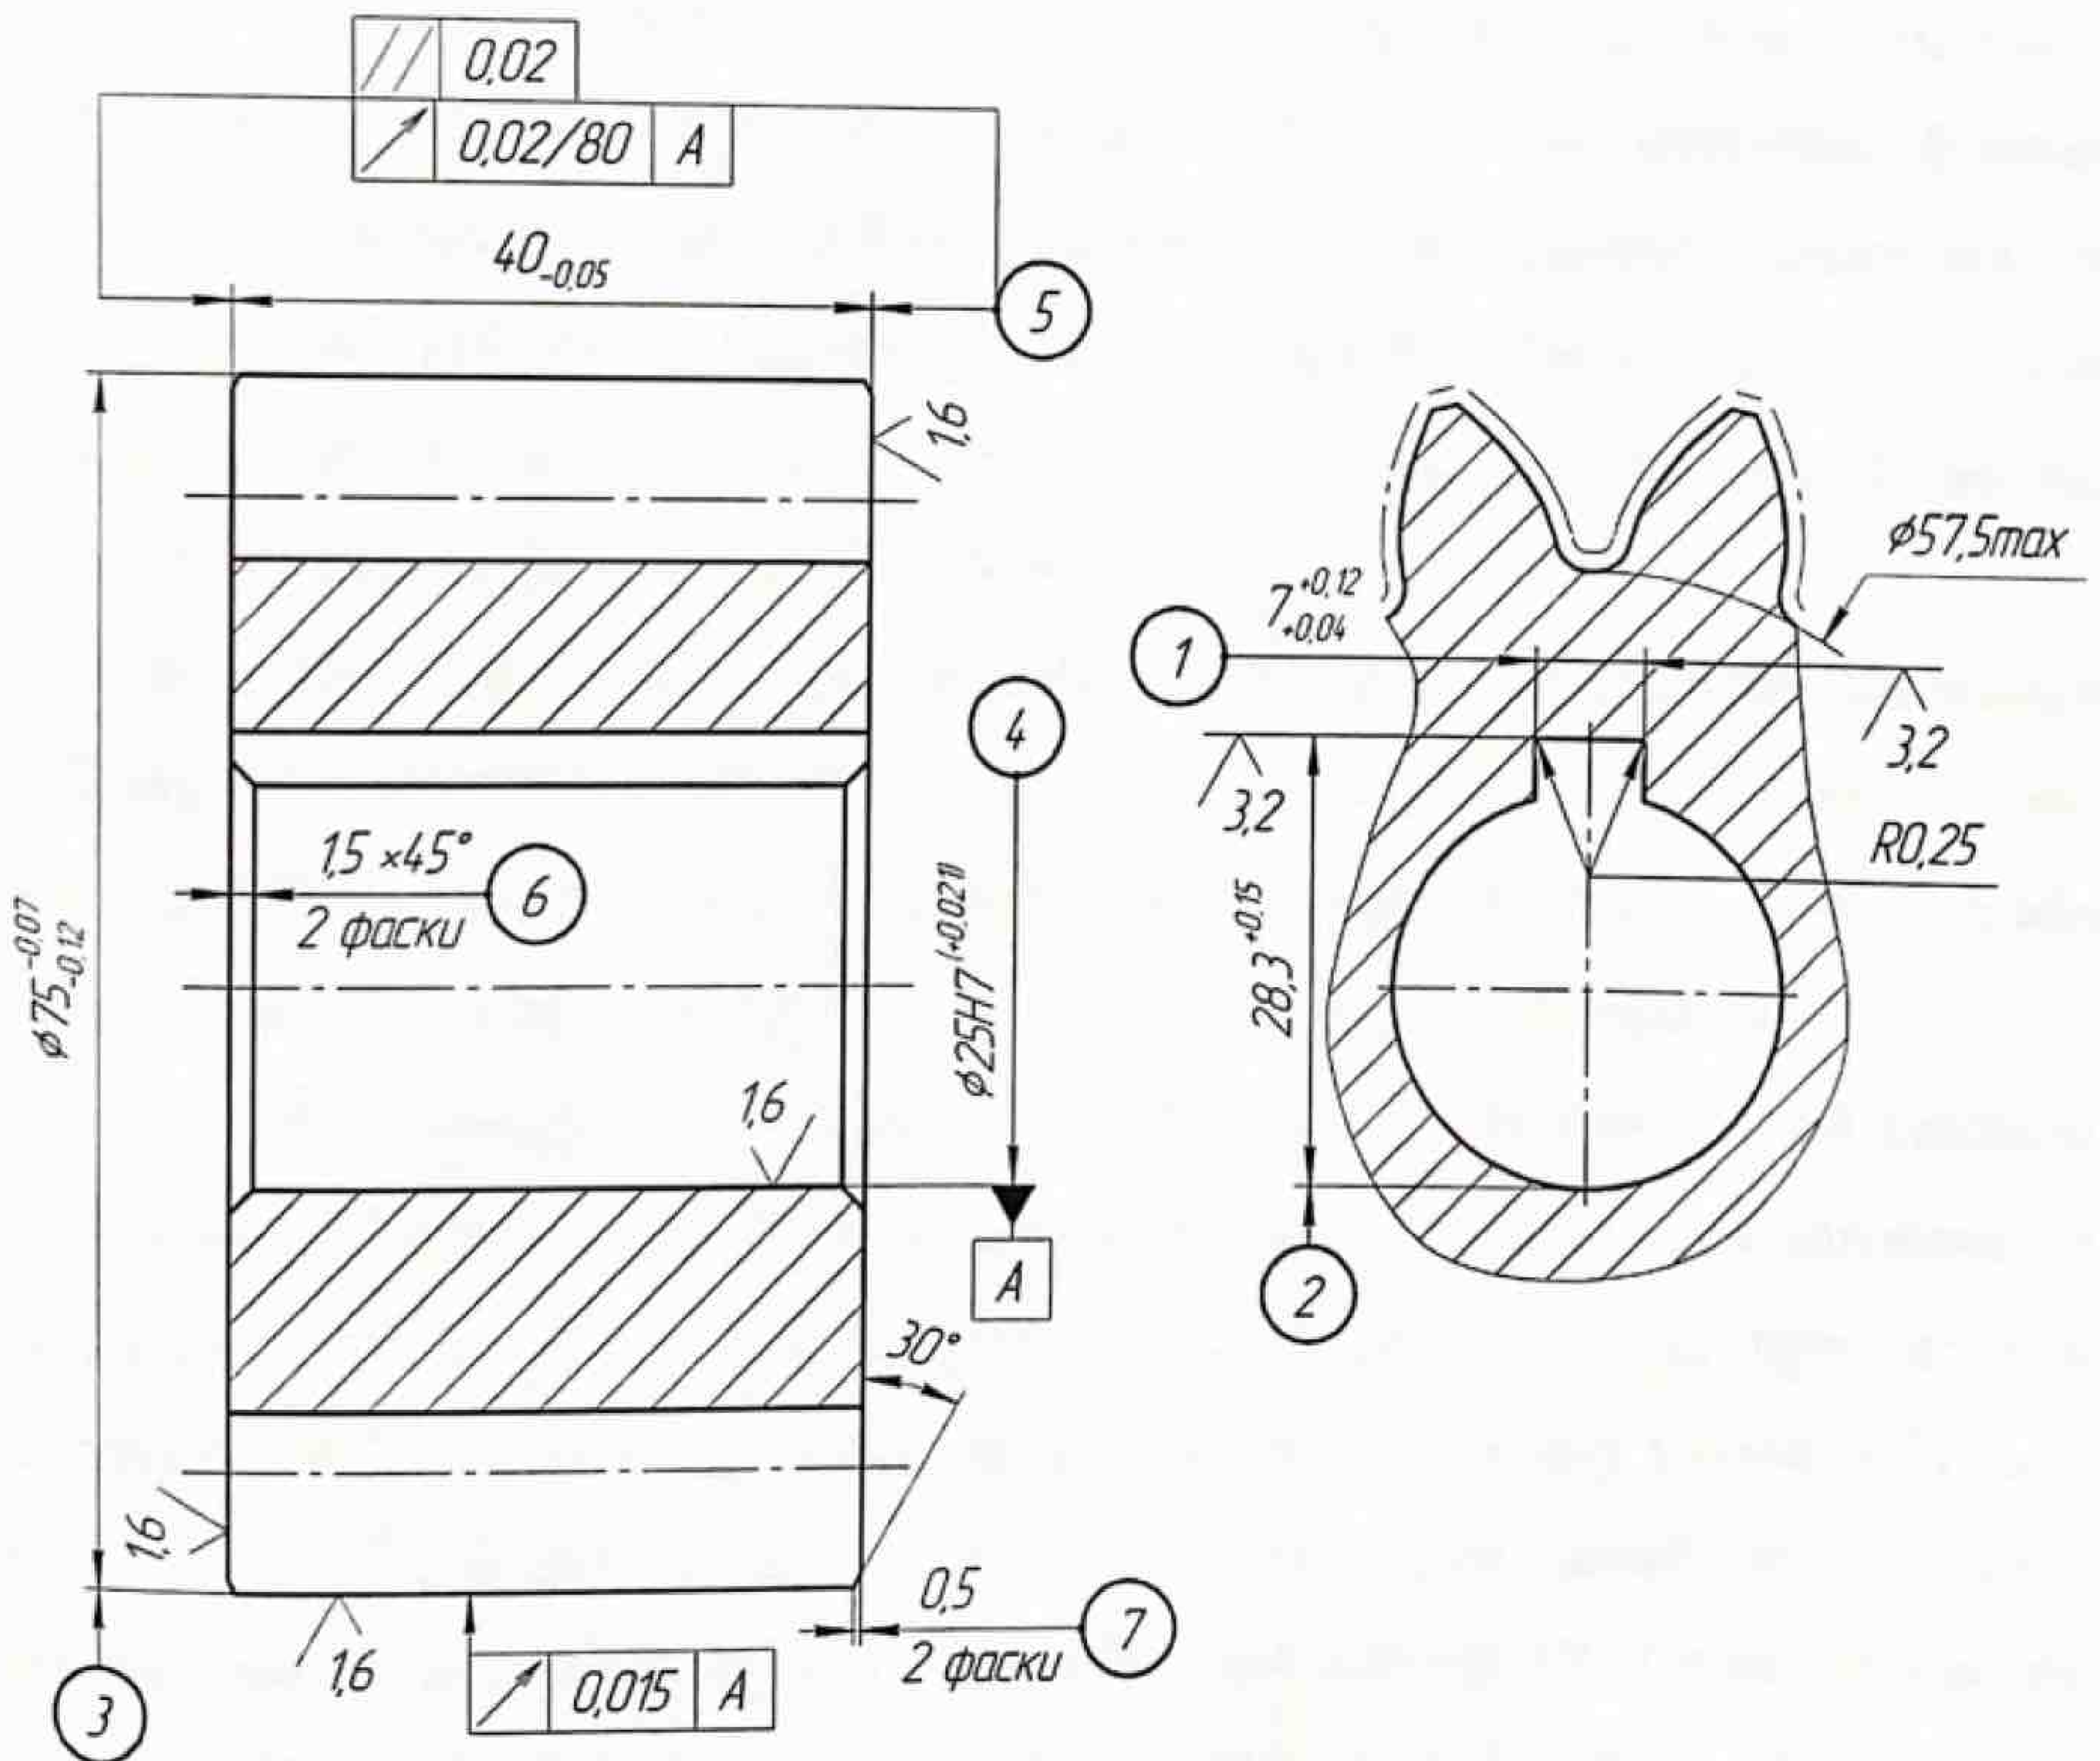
Ескіз деталі "шестерня" з нумерацією поверхонь
